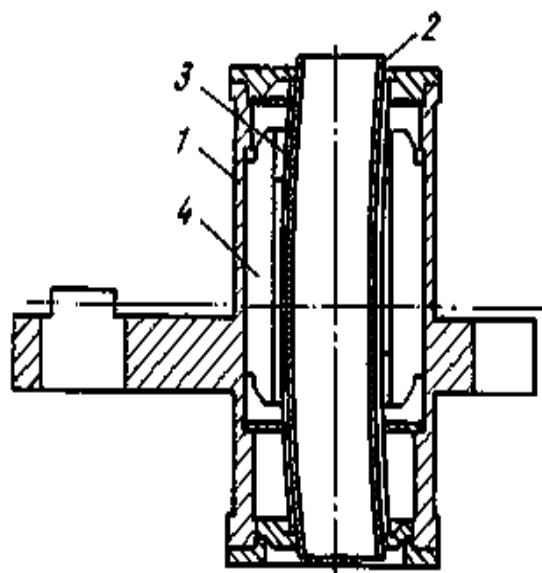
Схема кристаллизатора – ЭМП для отливки кордовой стали
